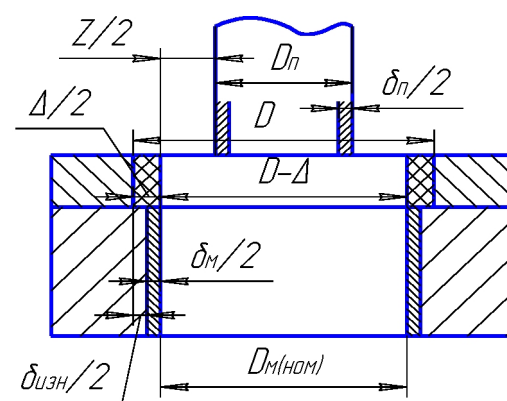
Схема расположения полей допусков на исполнительные размеры матрицы
